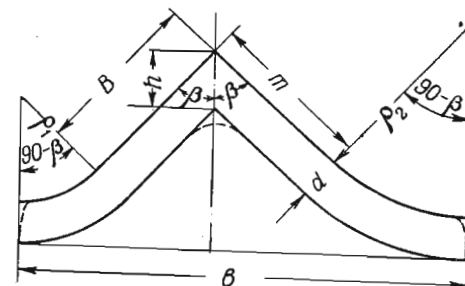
Схема формы углового калибра к выводу геометрических соотношений в калибре для прокатки неравнобокой стали
